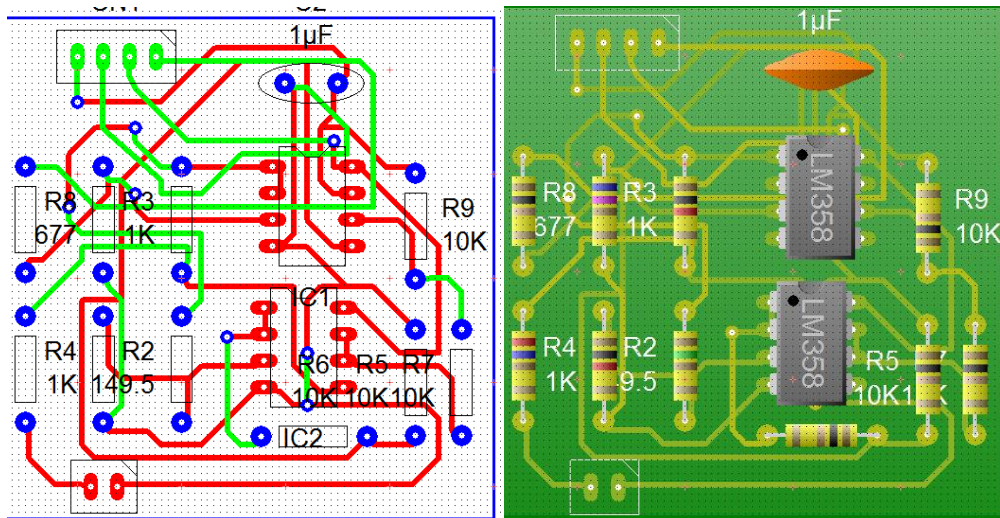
DISEÑO DEL PCB DEL MÓDULO ELECTRÓNICO DEL SENSOR
